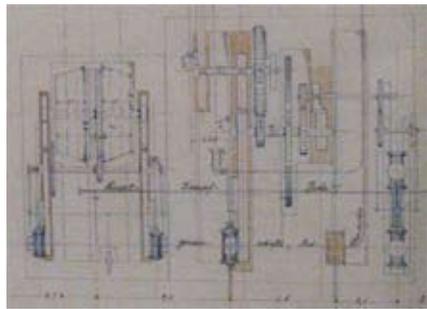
Maschinen des Kanekuhler Schachtes. 1875. Bergarchiv Clausthal links: die Zweizylinder-Fördermaschine mit 35,5 PS und doppelt konischer Seiltrommel in der Bildmitte: die Einzylinder-Wasserhaltungsmaschine, die über das Vorgelege das Kunstgestänge trieb rechts: ursprüngliche Anordnung der zwei „nassen“ Hubkolben-Kompressoren, angetrieben von der Wasserhaltungs-Dampfmaschine über ein zweites Vorgelege. Der zunächst geplante zweite Zylinder (rechts unten, hellbraun gezeichnet) wurde nicht benötigt und deshalb auch nicht gebaut.
